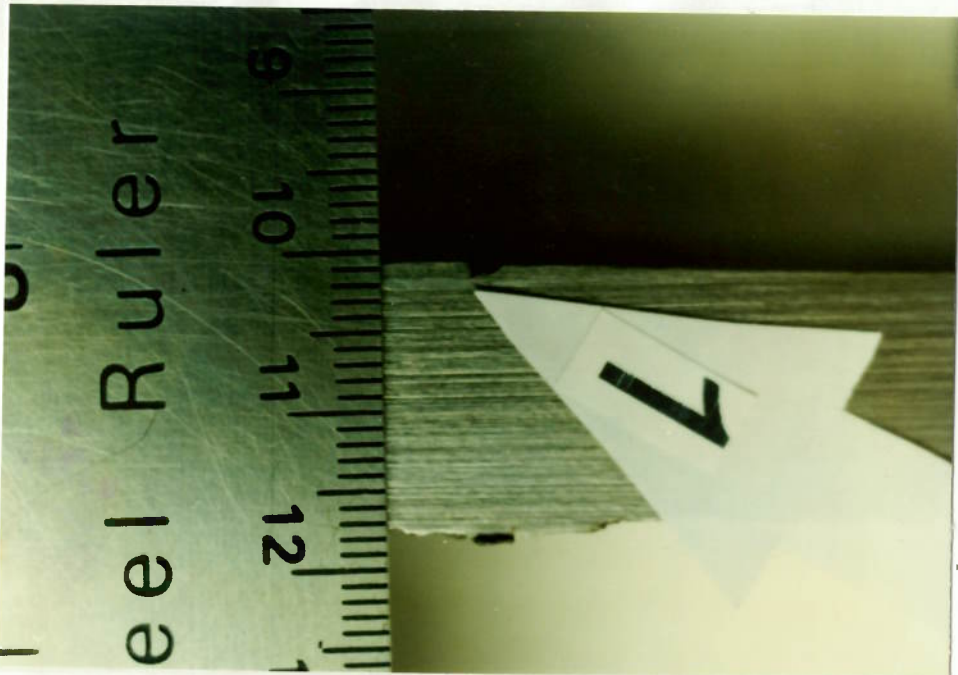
Detalhe da solda da chapa # 2 mostrando uma falta de penetração.
